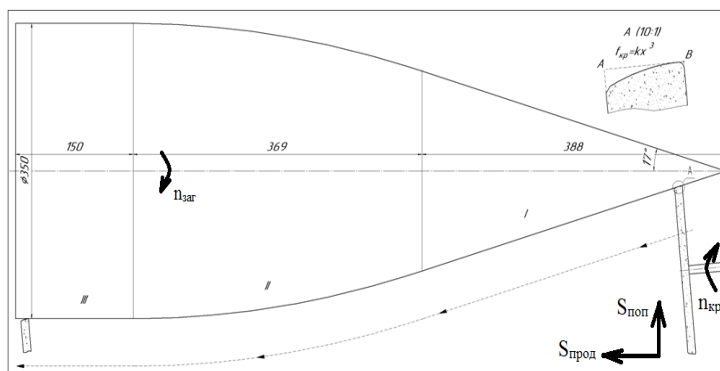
Схема обработки обтекателя шлифовальными кругами с неравномерным износом профиля круга
